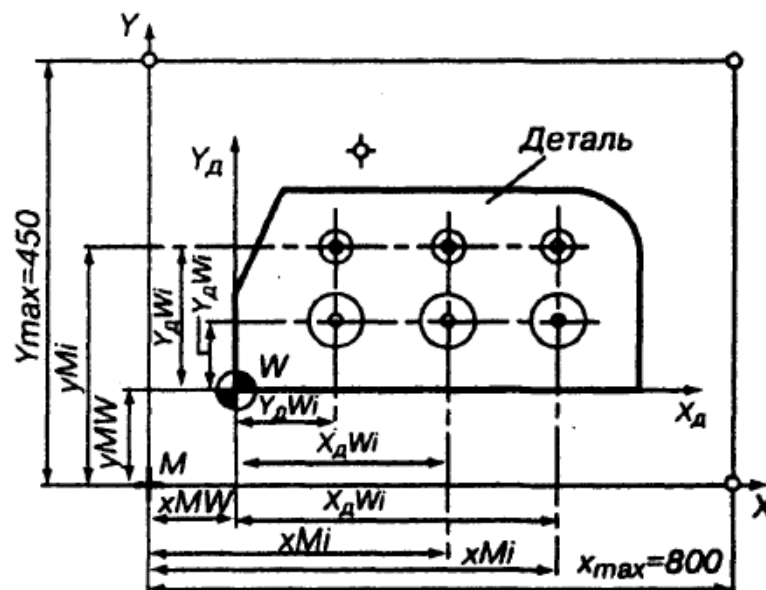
Система координат станка (XMY) и детали (Xd, W, Yd)
